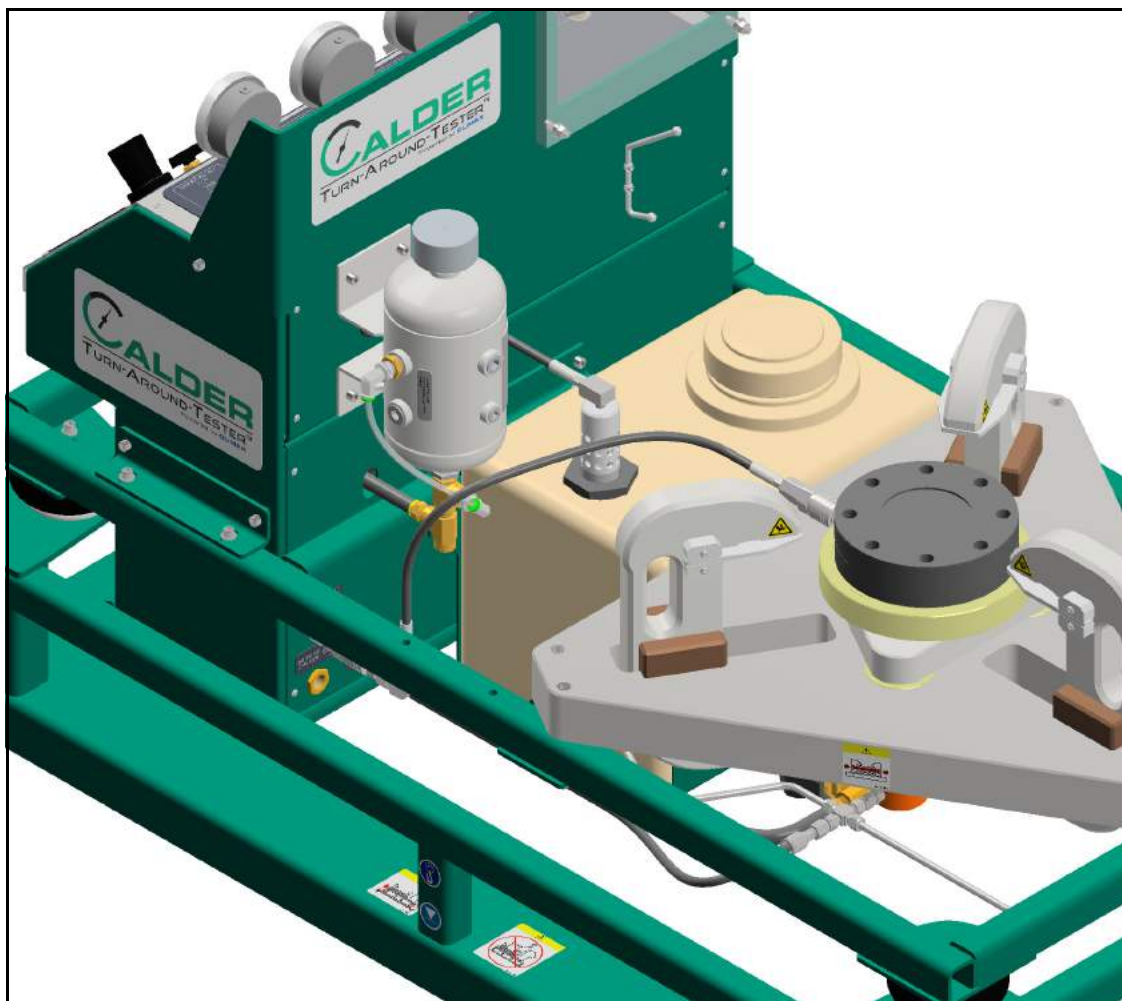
EMBLEMES DES ÉTIQUETTES À L'ARRIÈRE DU CÔTÉ GAUCHE
